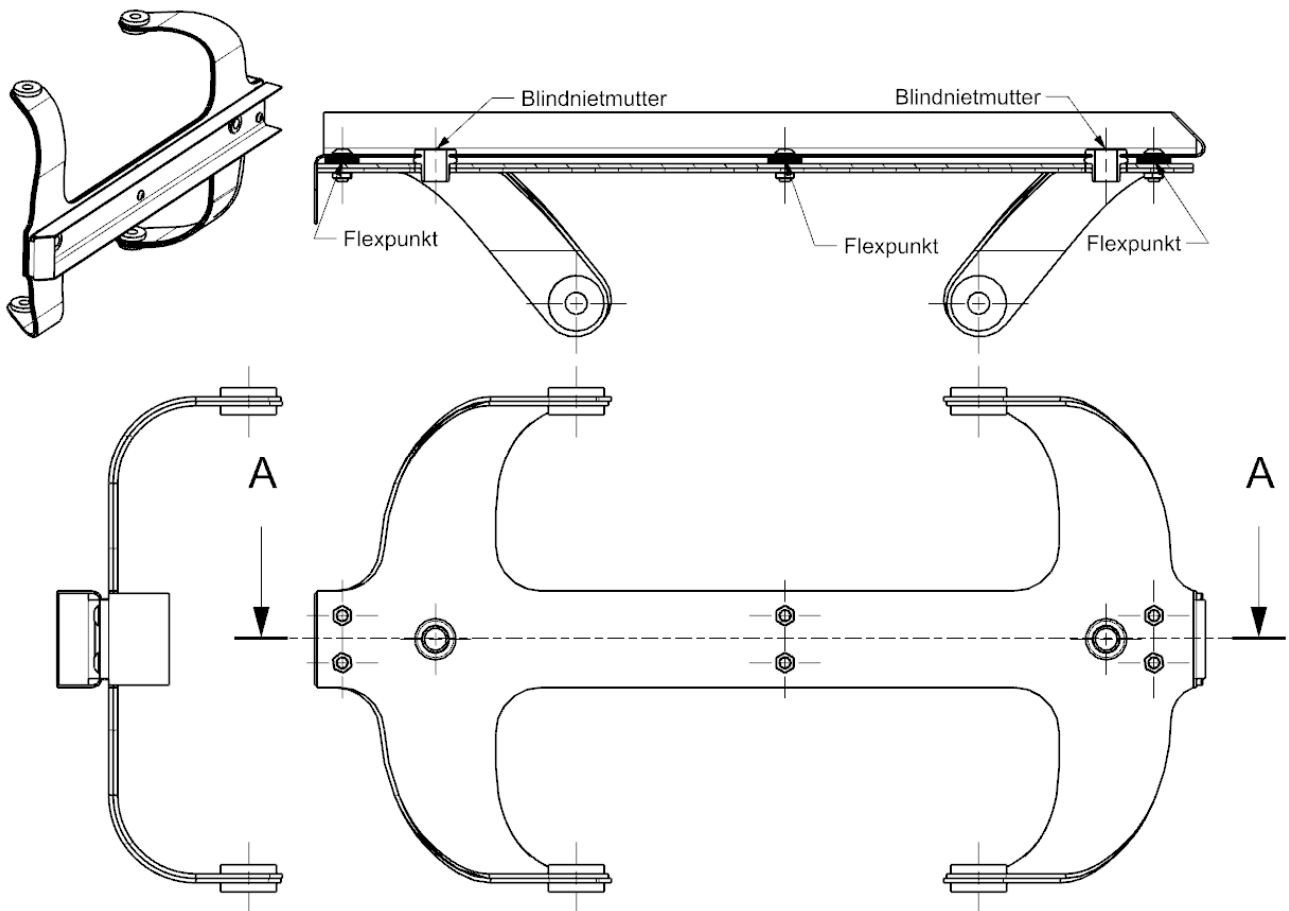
Stahlfeder aus gebogenem Blech mit Schweißteil verschraubt
